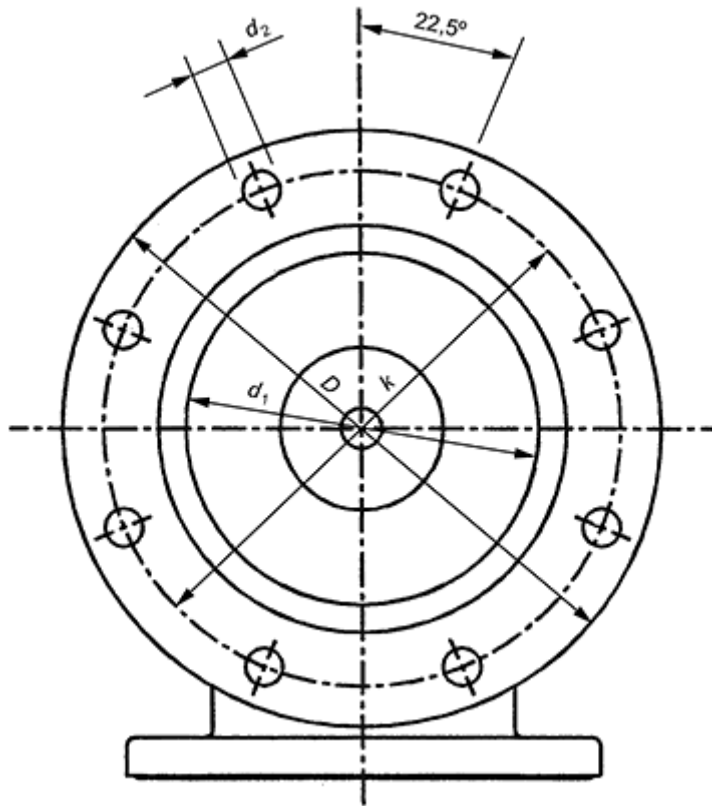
Присоединительные размеры монтажного фланца цистерны для приемного клапана
